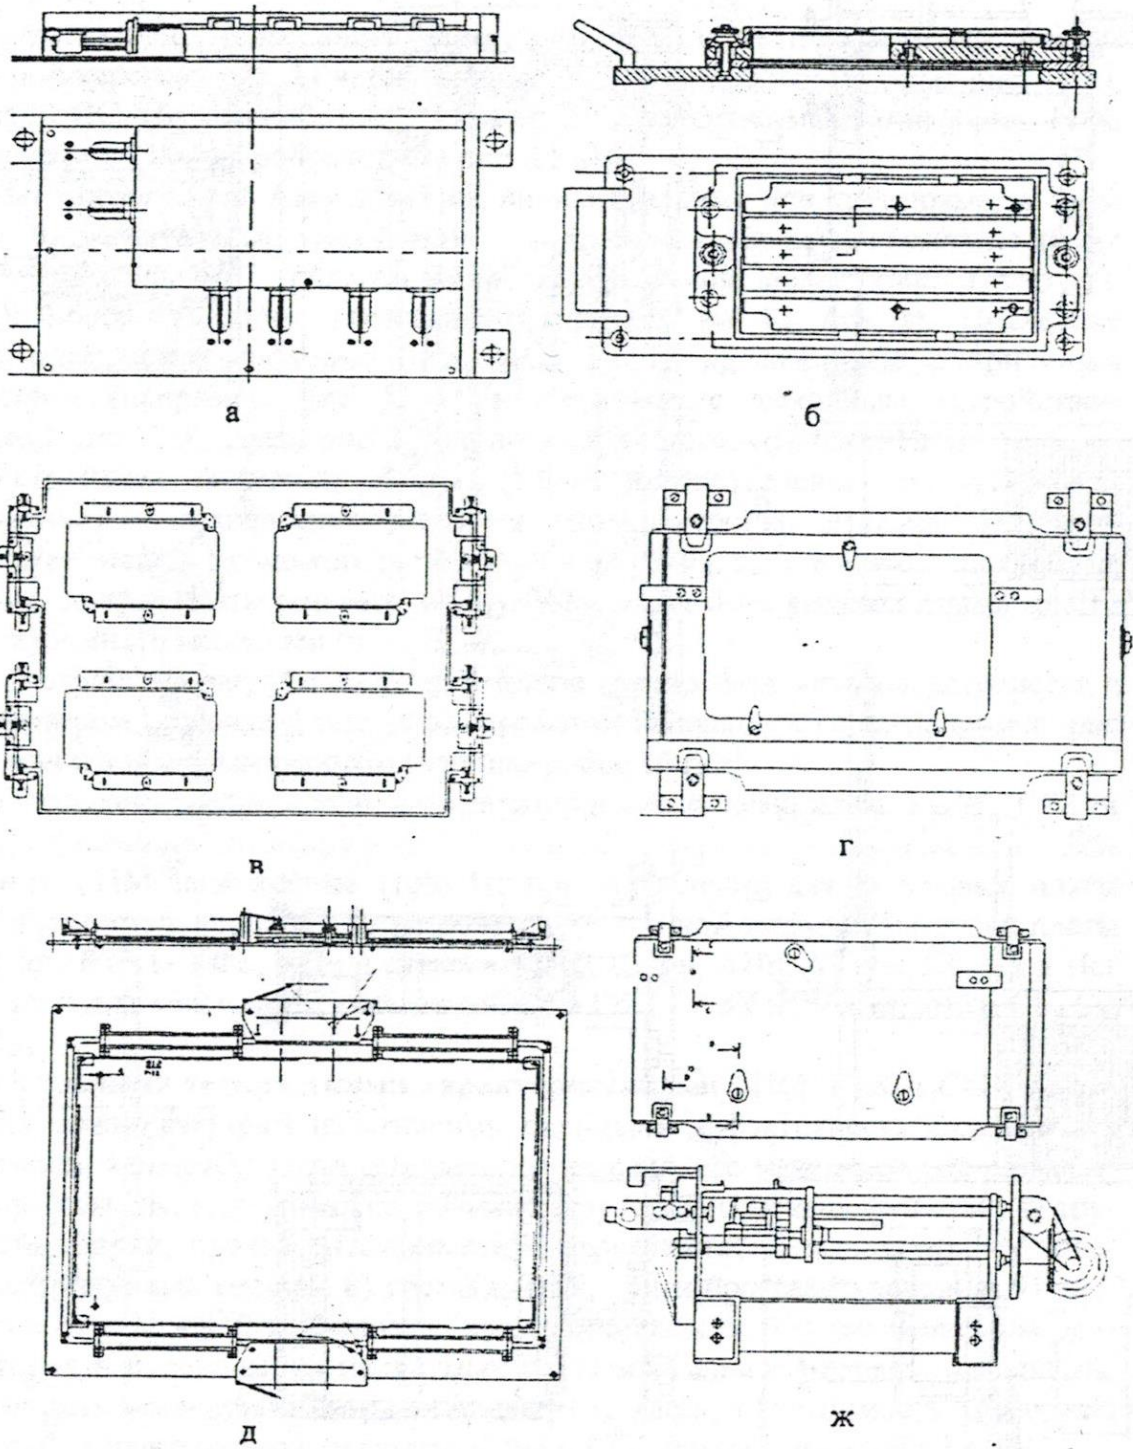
Примеры приспособлений для фиксации платы в зоне сборки
